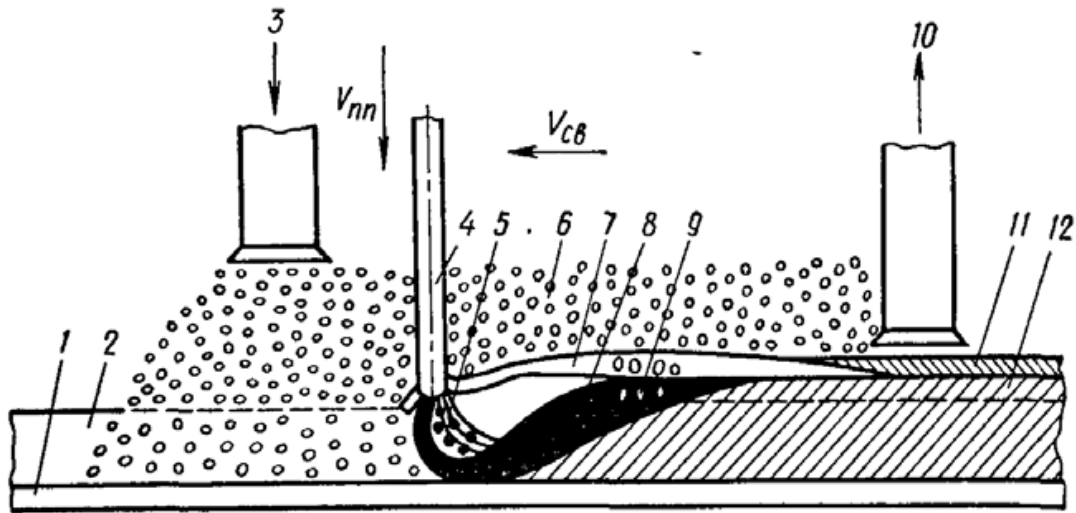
Схема процесу автоматичного зварювання під флюсом: 1 – підкладка; 2 – виріб; 3 – бункер під флюс; 4 – електрод; 5 – дуга; 6 – флюс; 7 – оболонка розплавленого флюсу; 8 – зварювальна ванна; 9 – гази; 10 – пристрій пневмовідсмоктувача нерозплавленого флюсу; 11 – шлакова кірка; 12 – метал шва
